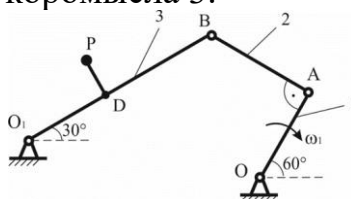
Схема механизма привода заключающих платин Р вязально-прошивной машины
